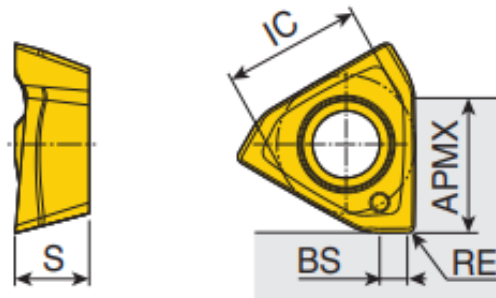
Загальний вид пластини 3P TF90- 12125-40R-15 до торцевої фрези TaeguTec
